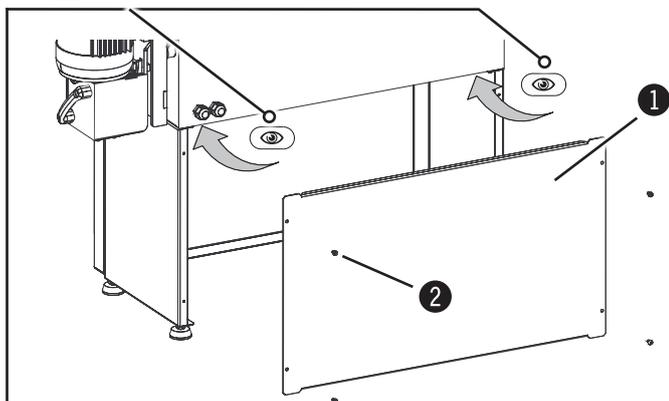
Подготовка - Смазать механизм регулировки высоты
